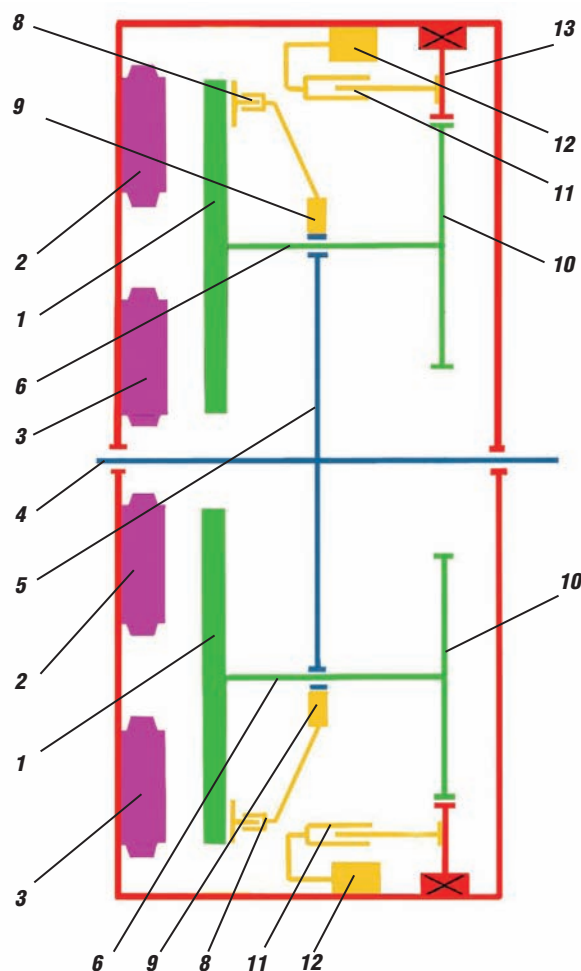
Устройство двухскоростного орбитального генератора: 1 — торцевые роторы; 2 — внешний статор; 3 — внутренний статор; 4 — вал водила; 5 — водило; 6 — оси роторов; 7 — корпус агрегата; 8 — фиксаторы роторов; 9 — приводы фиксаторов роторов; 10 — сателлиты; 11 — фиксаторы кольцевой шестерни; 12 — приводы фиксаторов кольцевой шестерни; 13 — кольцевая шестерня; 14 — кольцевой подшипник
